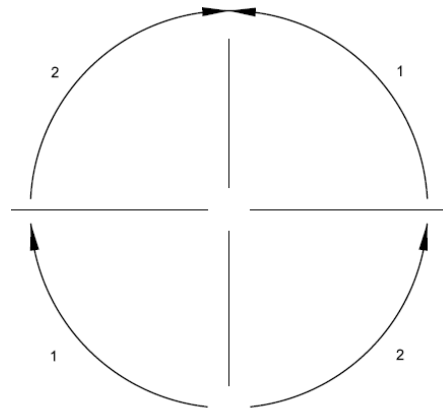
Secuencia de Soldaduras Circunferenciales
